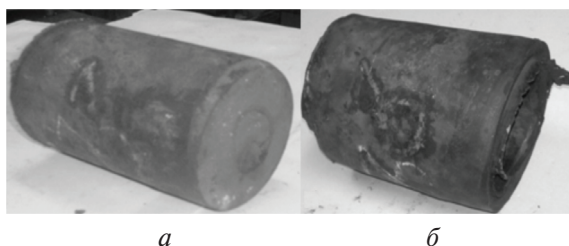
Фото задних концов обжатой заготовки и гильзы (заготовка с усеченным конусом и выпуклым торцом размером  $L = 40 \pm 5$  мм с  $R = 250$  мм)
